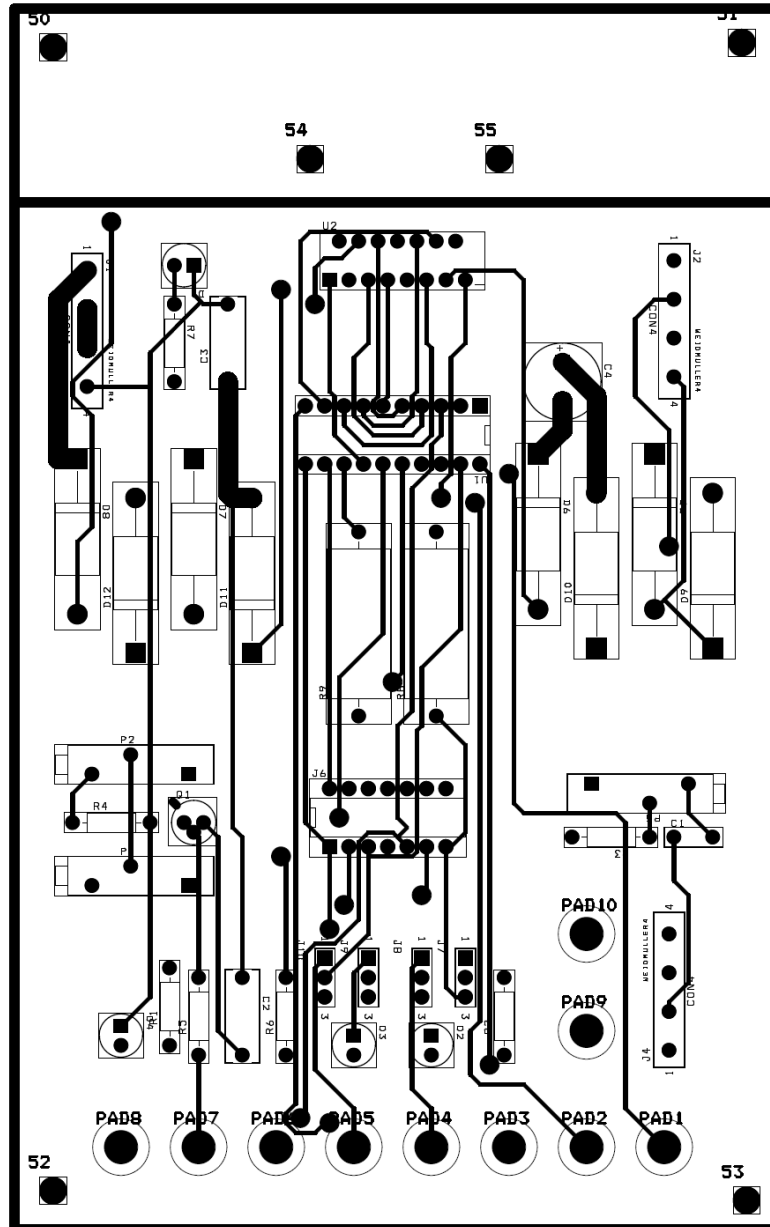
Capa inferior (BOT) de la PCB de la interfície per al motor bipolar
